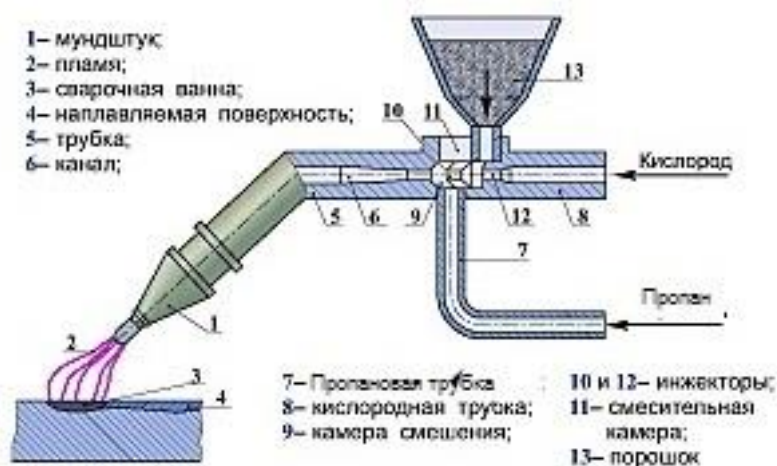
Устройство газовой горелки для наплавки порошка
